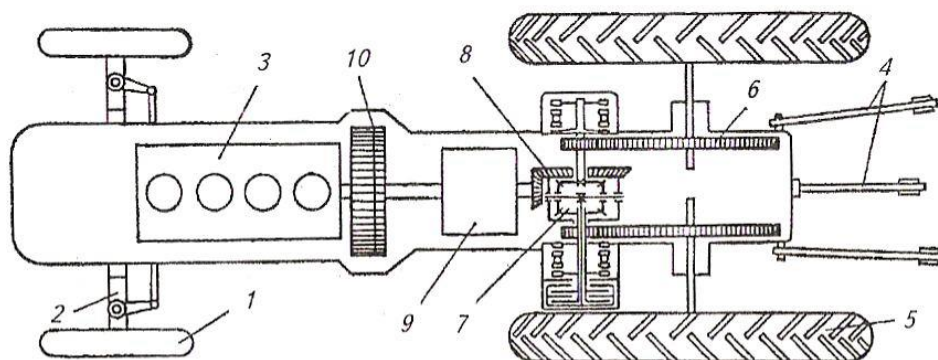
Схема расположения основных частей, механизмов и деталей колесного трактора:
